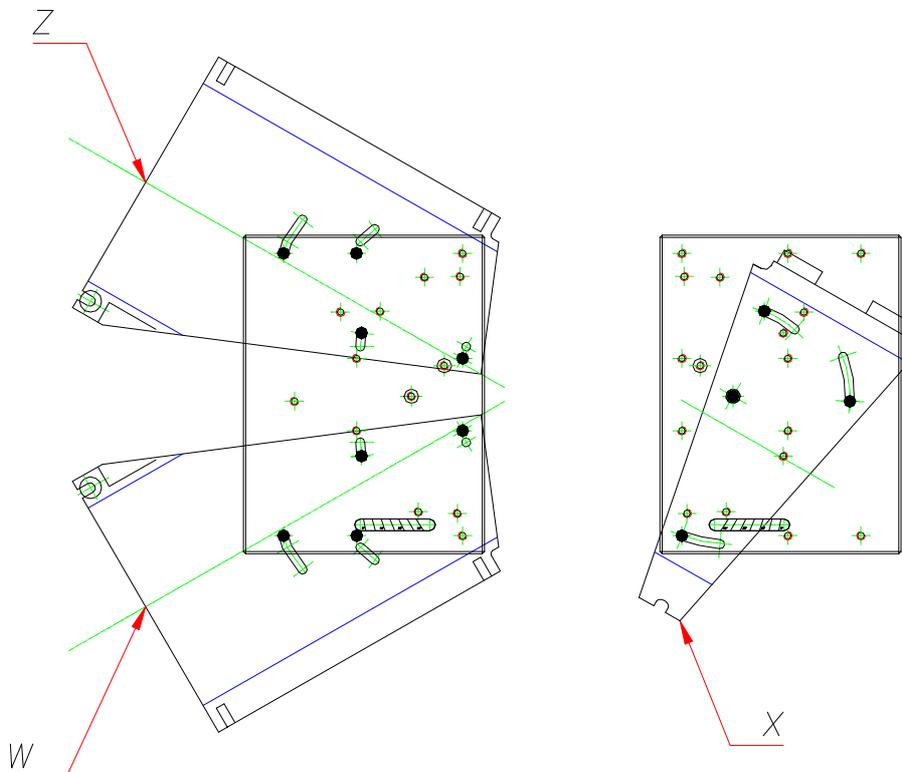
Крепление зажимов для второго шва Y-тройников 60°
